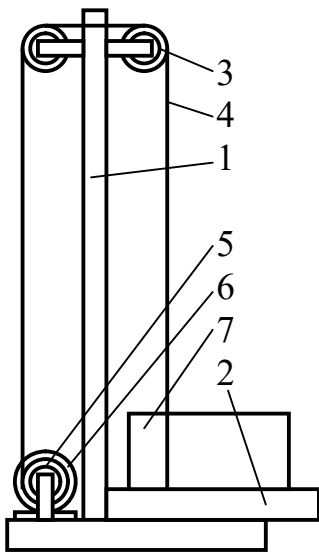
Схема підйомника: 1 – ферма; 2 - платформа; 3 – шків; 4 – троси; 5 - барабани; 6 - електродвигун; 7 - контейнер із заготовками
